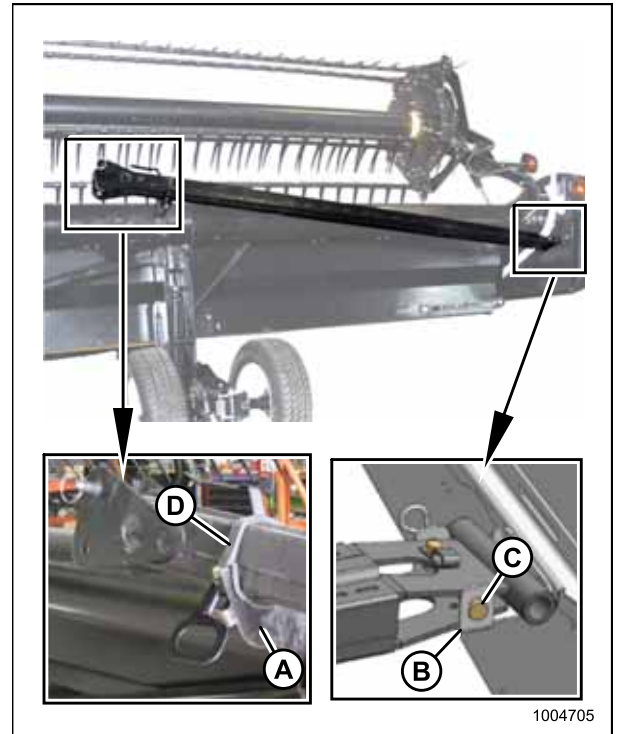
Extracción de la barra de remolque - Lado derecho
